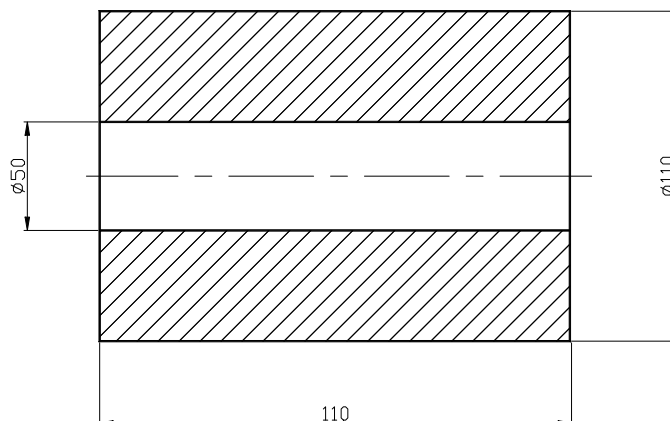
Ескіз заготовки із трубного прокату
